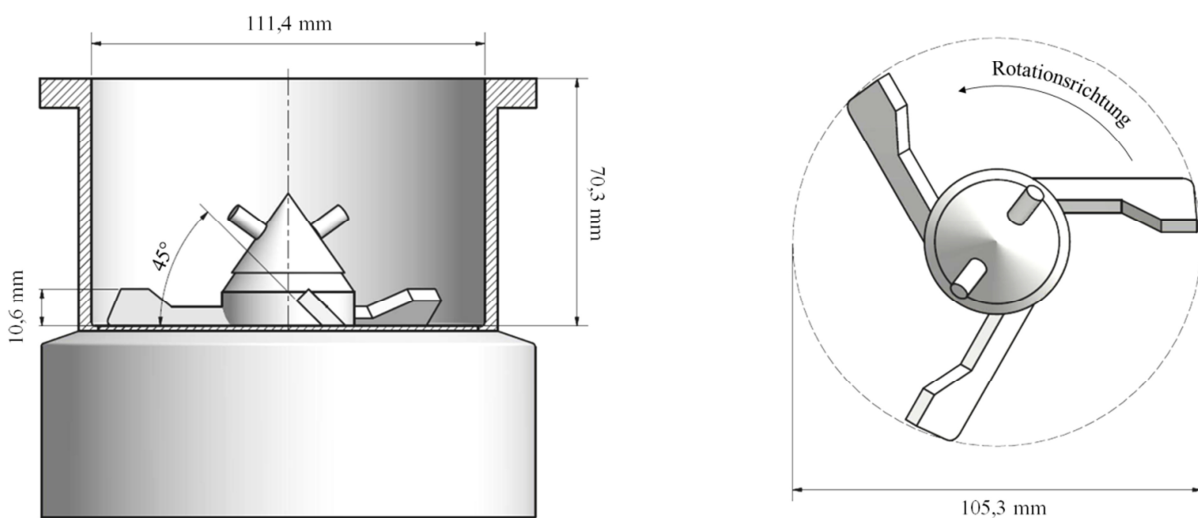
CAD Zeichnung des Mischbehälters und Mischwerkzeugs inklusive der zugehörigen geometrischen Abmessungen.
